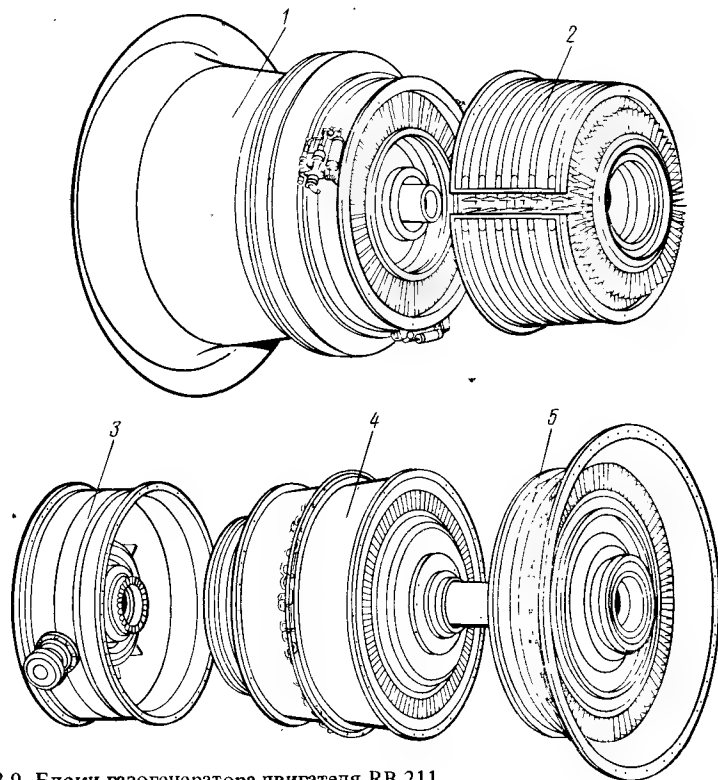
Блоки газогенератора двигателя RB.211.
